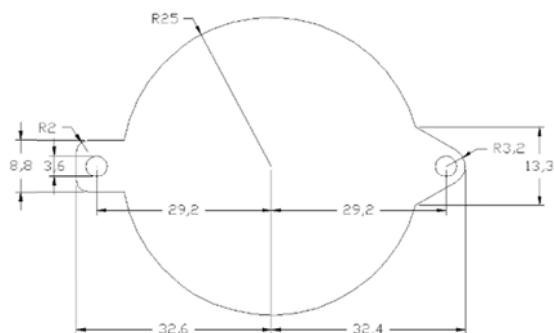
Соединительный фланец передатчика - тип SENIOR
